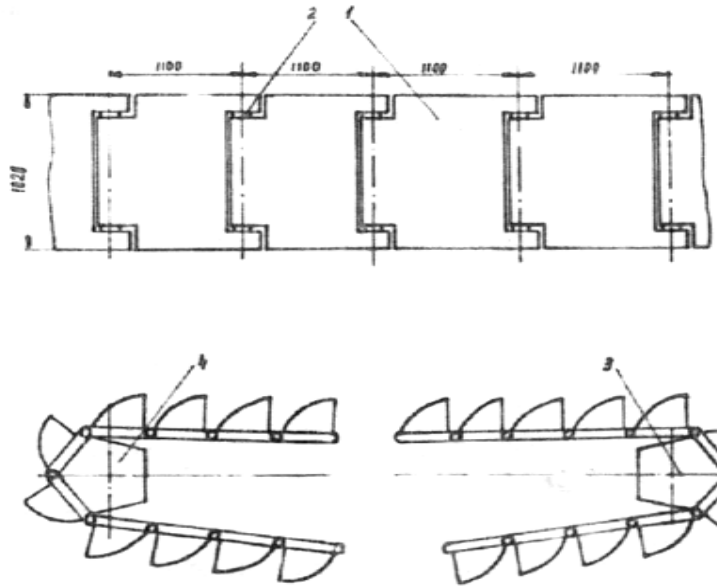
Розрахункова схема ковшового ланцюга землечерпалки:
